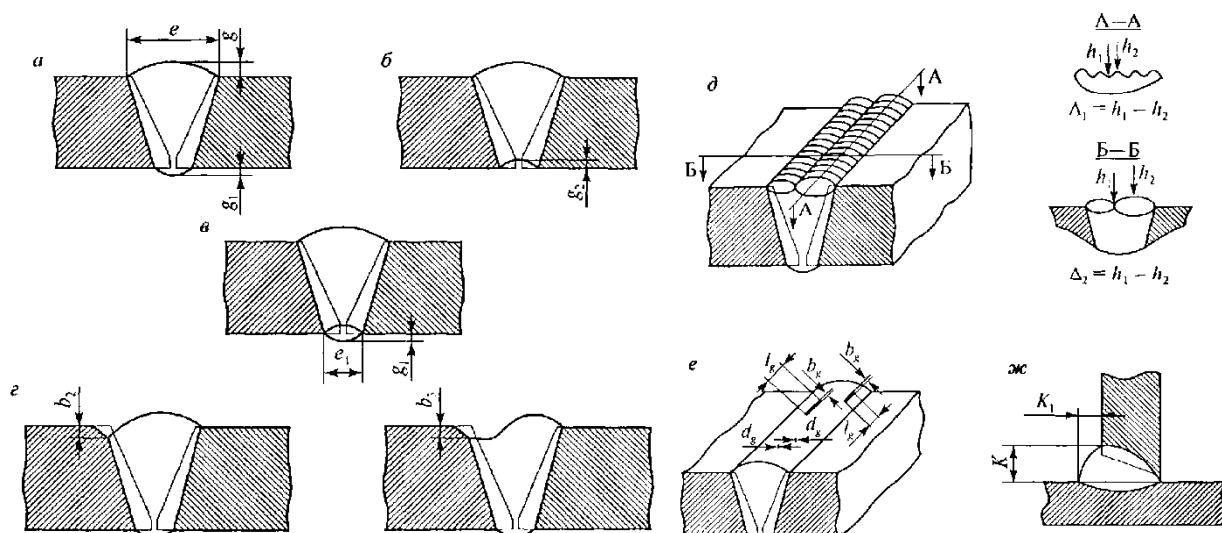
Конструктивные элементы и дефекты сварного шва, подлежащие измерительному контролю: а, б – размеры (ширина, высота) стыкового одностороннего шва с наружной и внутренней стороны; в – то же двухстороннего сварного шва; г – подрез и неполное заполнение разделки кромок; д – чешуйчатость ($\Delta 1$) шва и западание между валиками шва ($\Delta 2$); е – размеры поверхностных включений (диаметр – dg; длина – lg; ширина – bg включения); ж – размеры катета шва углового (таврового, нахлесточного) соединения
